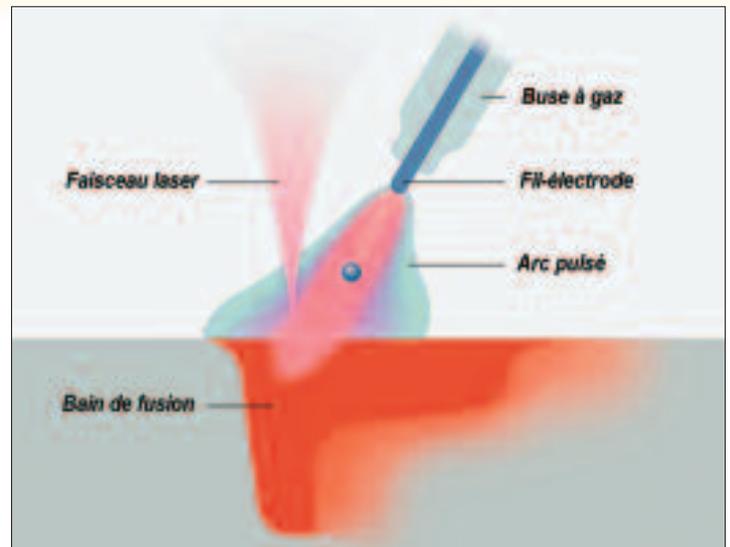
Schéma du procédé de soudage au laser hybride – source: Fronius (Autriche)
